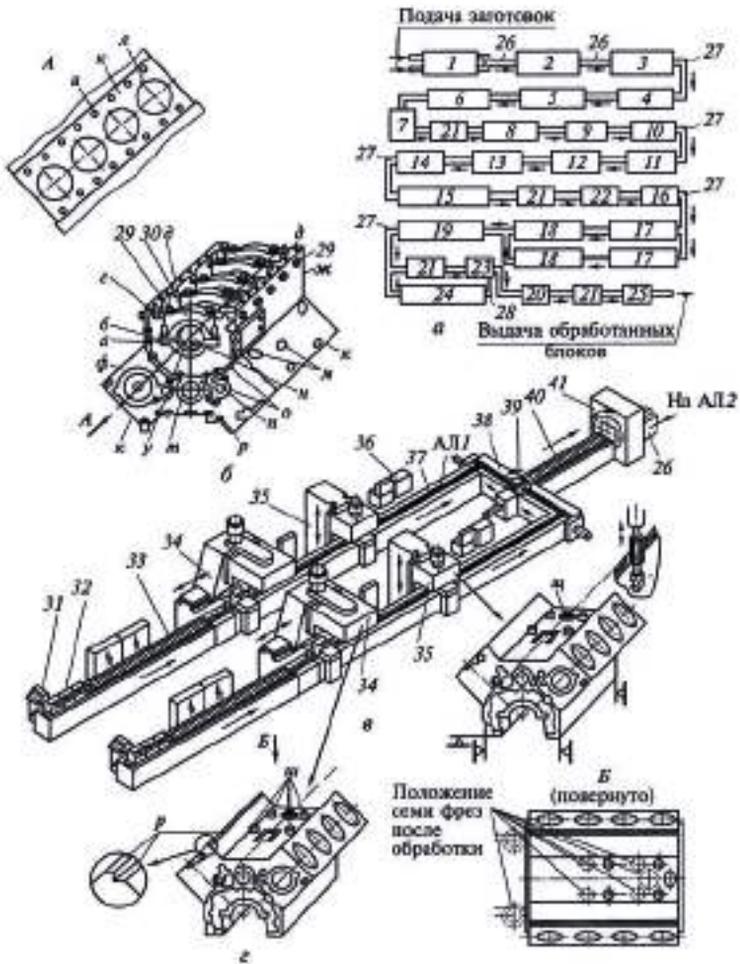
САЛ для обработки блока цилиндров дизельного двигателя автомобиля КамАЗ: а – планировка САЛ; б – блок цилиндров; в – АЛГ; г – технологический процесс обработки; 1-20 – автоматические линии; 21 – моечный агрегат; 22-25 – автоматизированные участки; 26, 27, 28, 37, 38 – шаговые конвейеры; 29 – болты для установки крышки; 30 – крышка; 31 – пульт; 32 – заготовка; 33, 40 – конвейеры-накопители; 34, 35 – станки; 36 – станция централизованной смазки; 39 – поворотный стол; 41 – барабан
